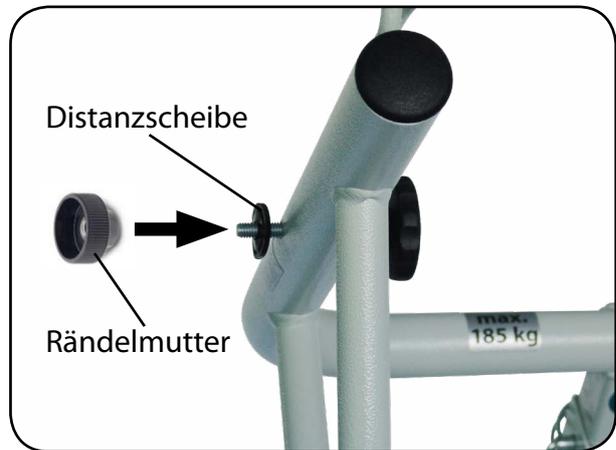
Rändelmutter aufschrauben
